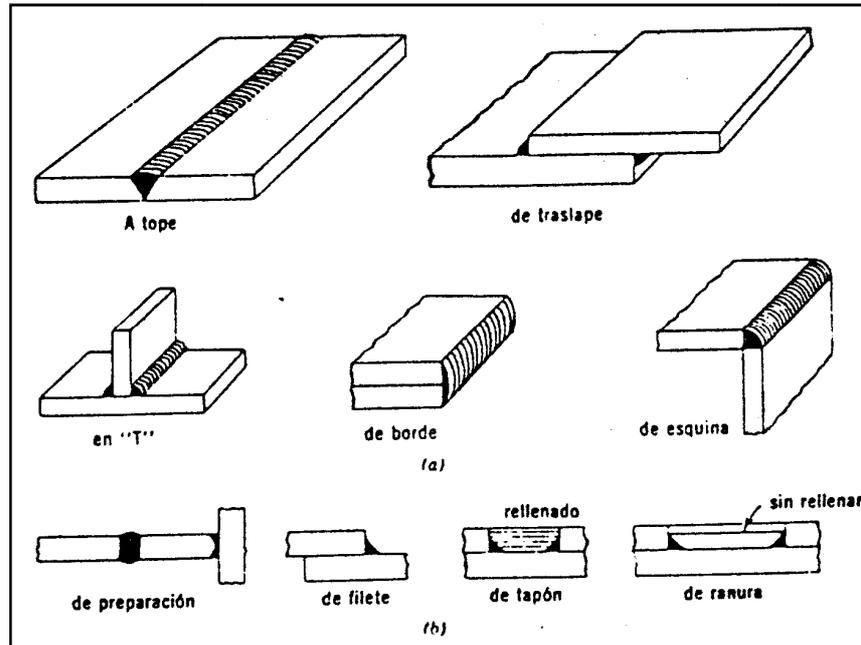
Conexiones soldadas: (a) tipos de juntas, (b) tipos de soldaduras
